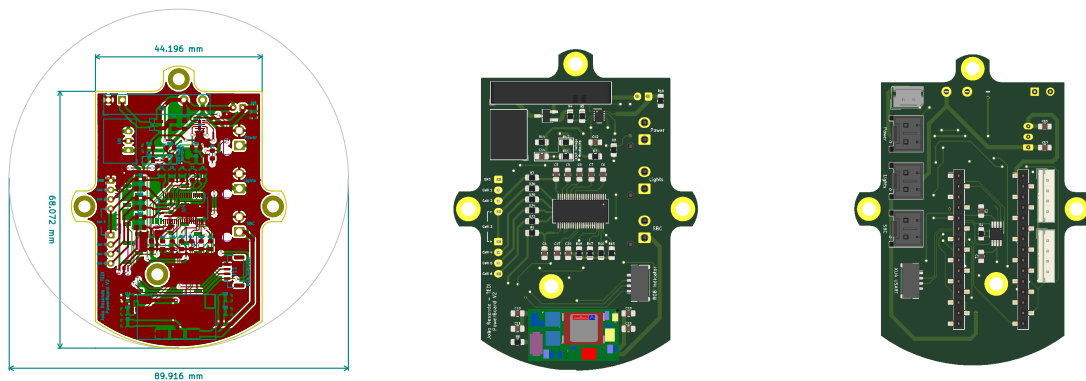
Dimensão e visão superior e inferior da PCB do BMS.
